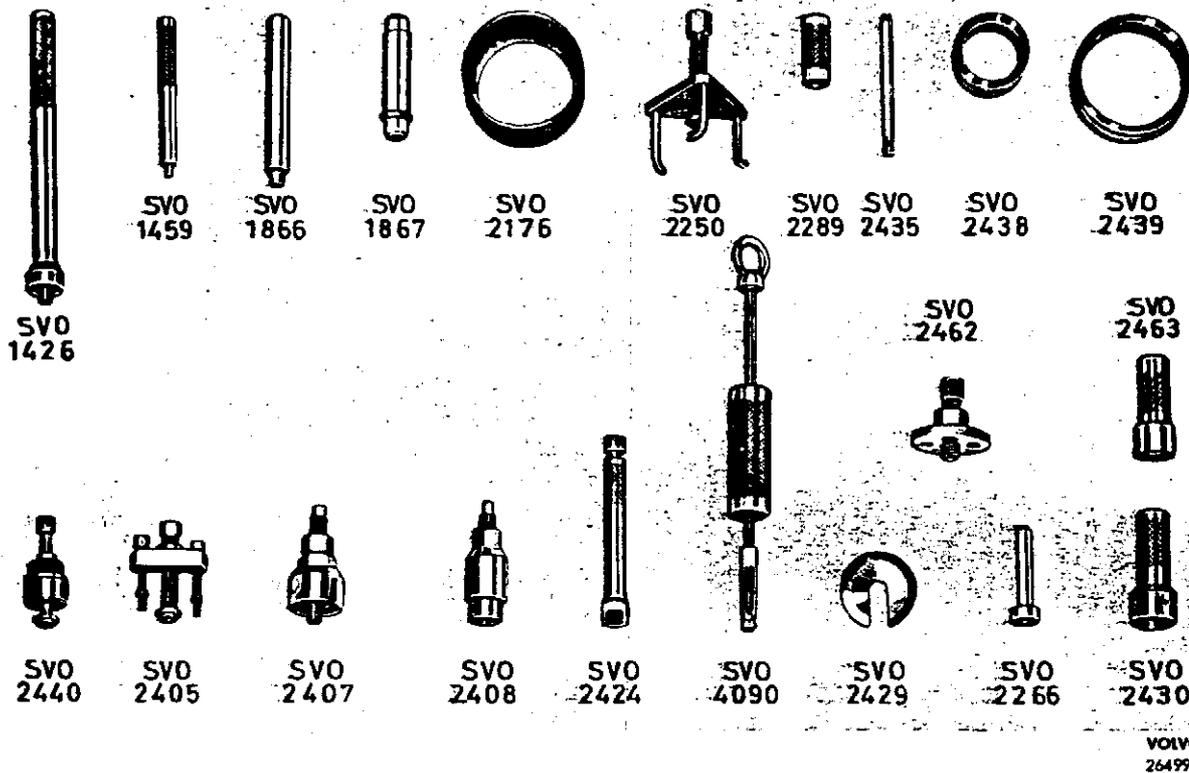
Spezialwerkzeuge für den Motor und die Wasserpumpe
